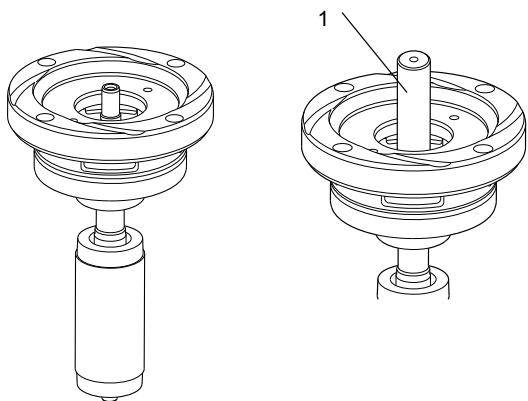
Установка нижнего подшипника в нагретый корпус масляной камеры
